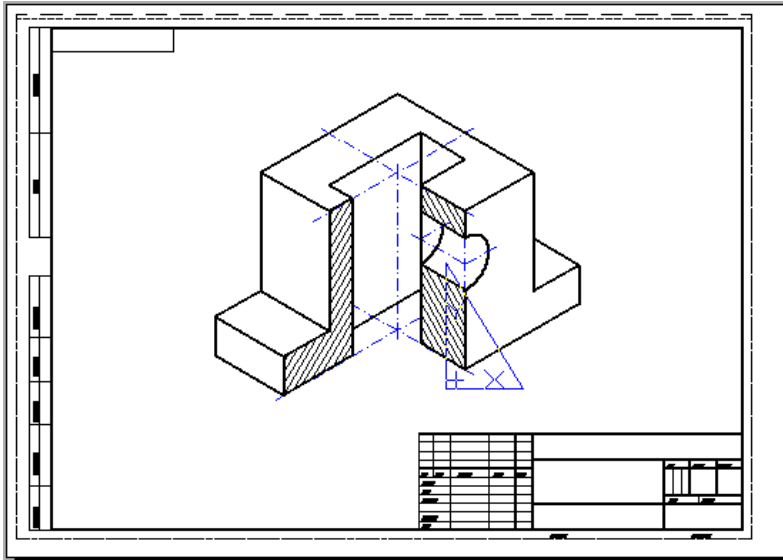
Аксонометрія деталі «Корпус»
